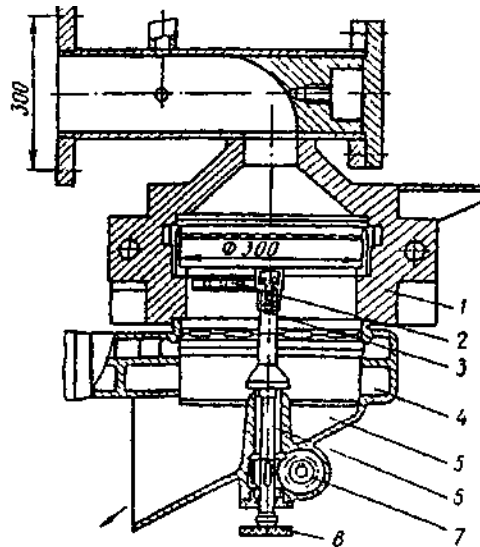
Пресова головка з механізмом різання коротких виробів по диску матриці
